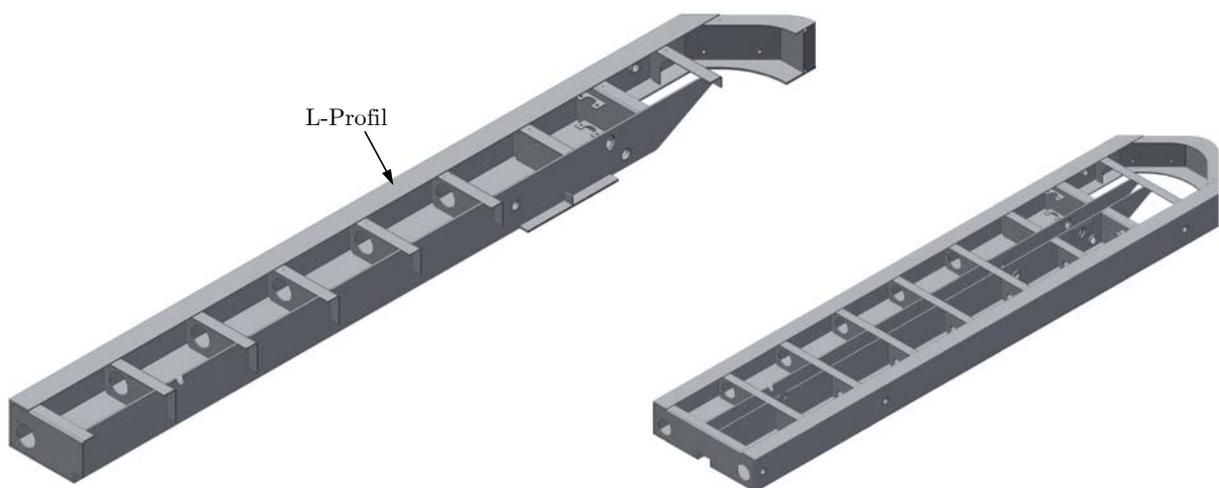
Laden-Schweißbaugruppe (Voll- und Schnittansicht von hinten)
